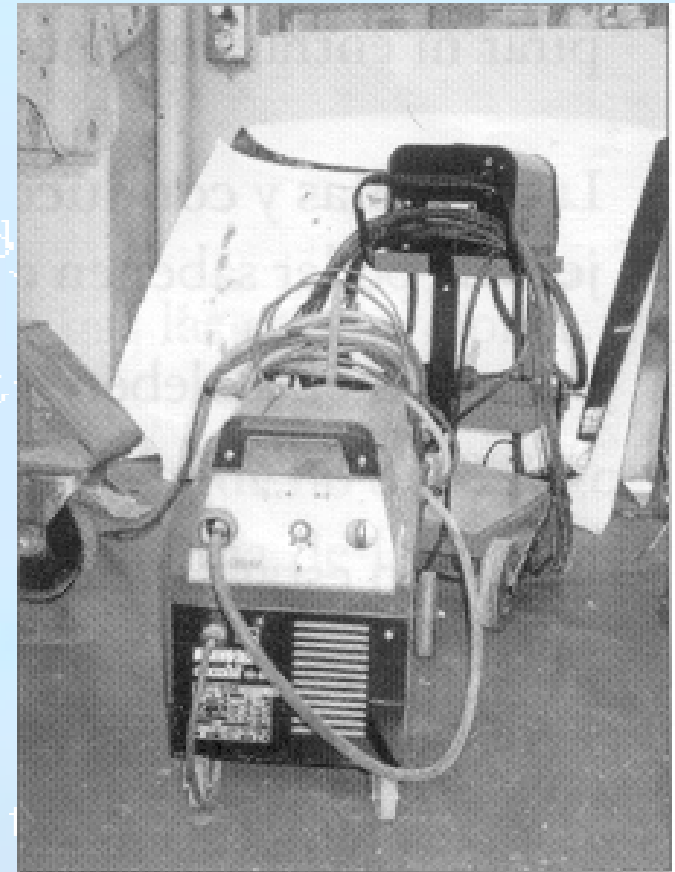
Soldadura eléctrica por arco y gas.
